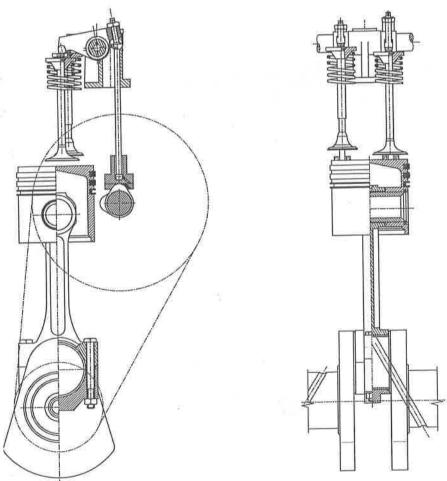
El mecanismo biela-manivela. Motor de explosión.
